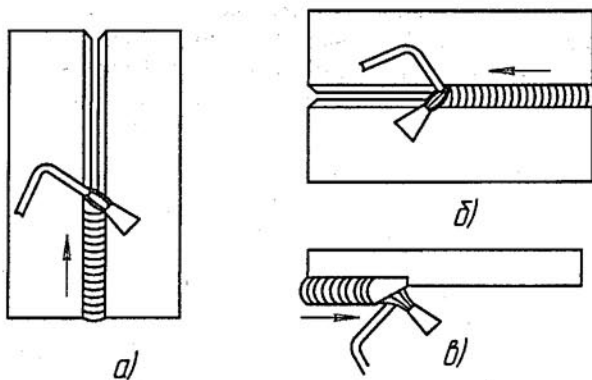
Схеми горизонтального і вертикального способів зварювання
